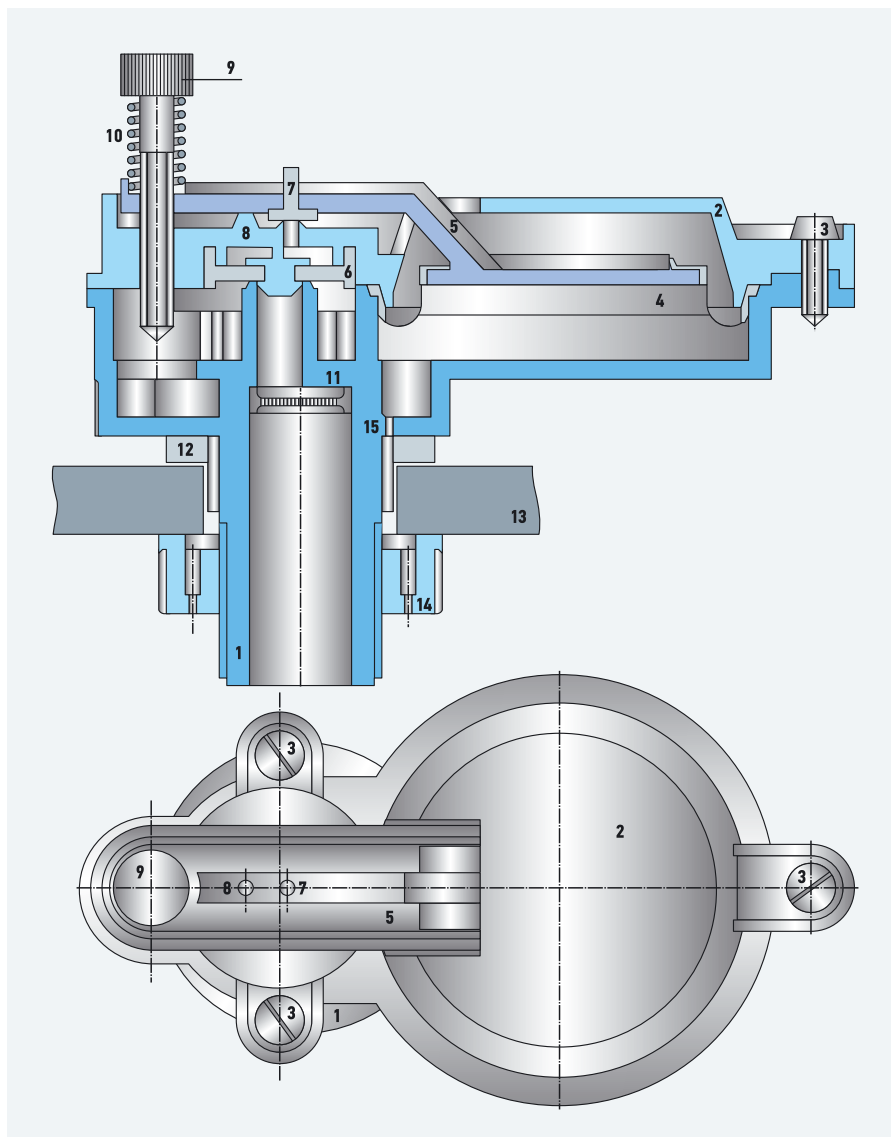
Конструктивная схема бесплавковой наполнительной арматуры с сервоуправлением с нижней подводкой (1 — корпус; 2 — крышка; 3 — крепежные шурупы; 4 — мембрана; 5 — рычаг; 6 — диафрагма с жестким центром; 7 — прокладка сервоклапана; 8 — ось поворота рычага; 9 — регулировочный винт; 10 — цилиндрическая пружина; 11 — поверхностный щелевой фильтр; 12 — уплотнительная прокладка; 13 — дно смывного бачка; 14 — крепежная гайка с отверстиями)
